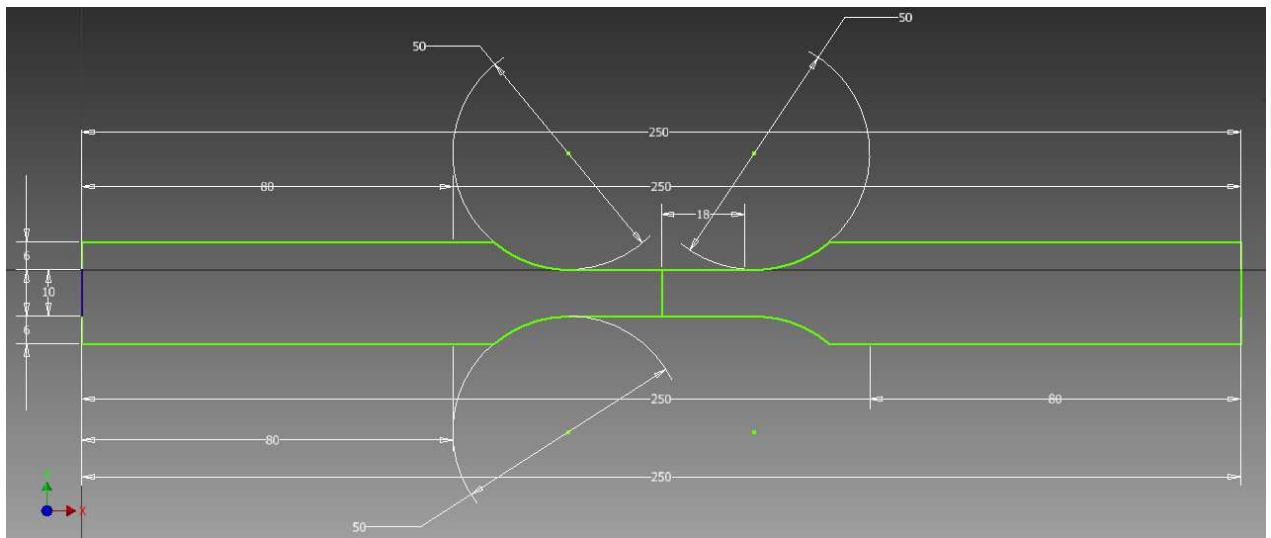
Dimensiones de una probeta para un ensayo de tensión
